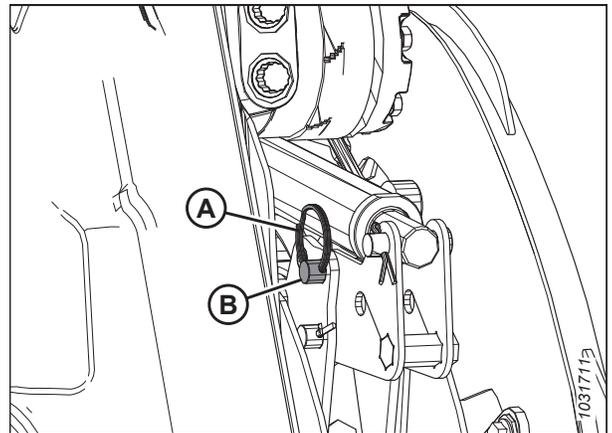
Cilindro del braccio centrale – Posizione avanzata
